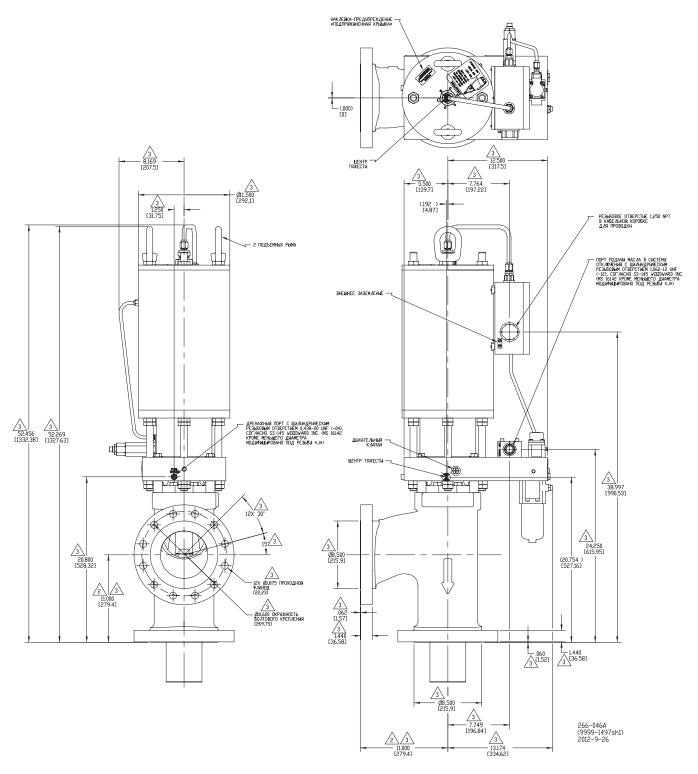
а. Габаритный чертеж регулятора SonicFlo (6 дюймов, класс 300)
